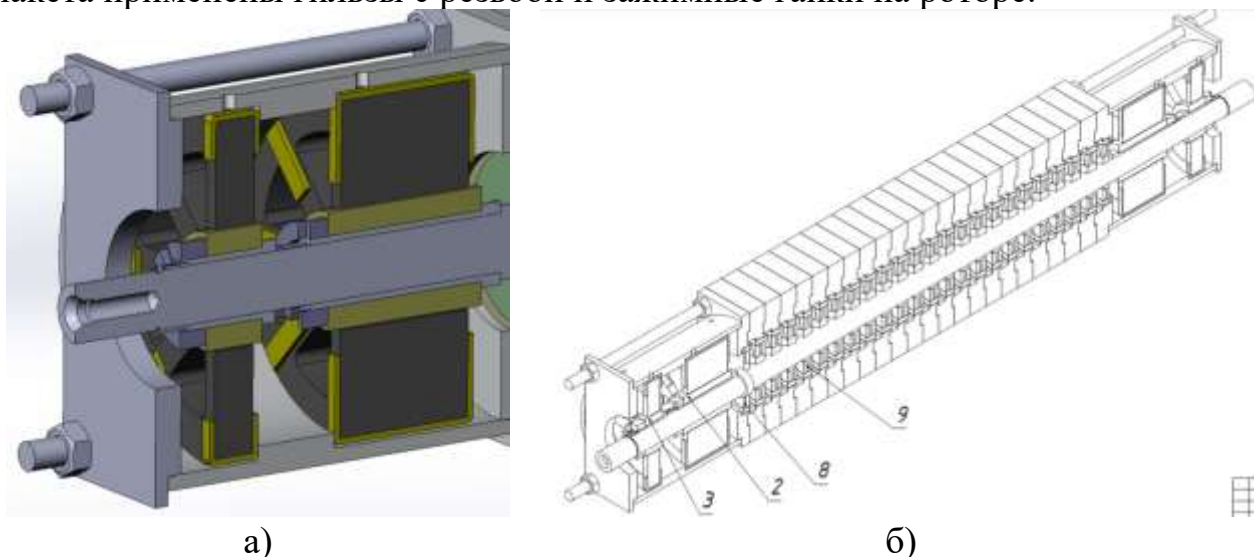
Трехмерная модель магнитного подвеса (а) и эскиз сборки генератора (б)
